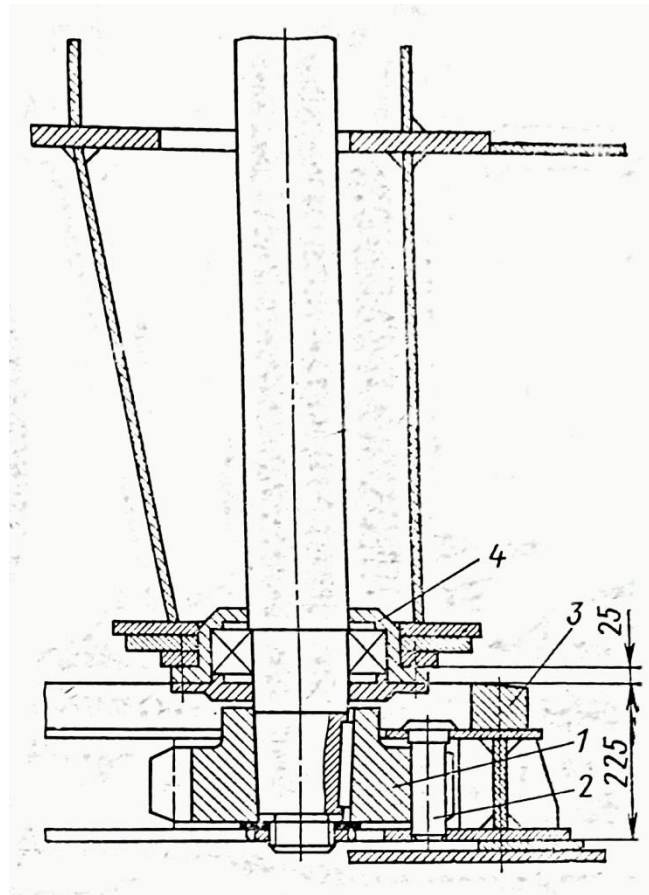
Радіально-упорний підшипник поворотного крана блокової конструкції на колоні
